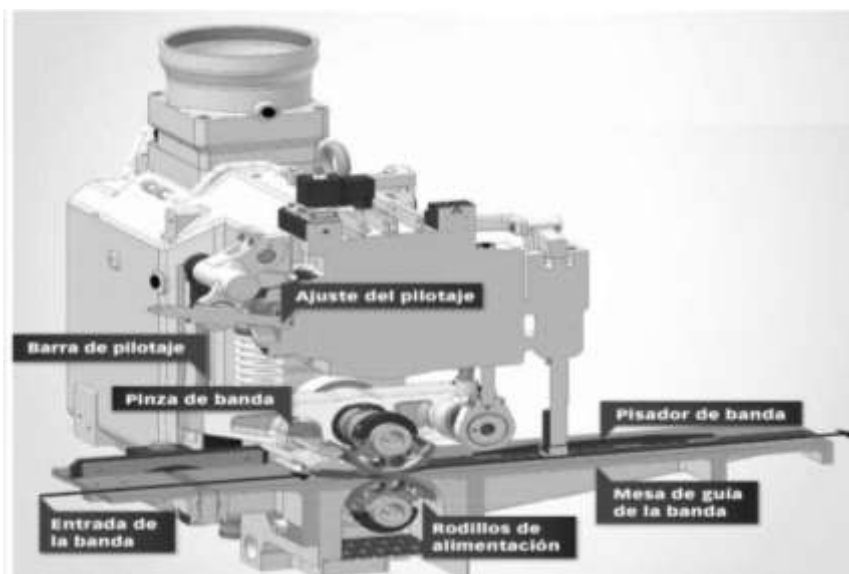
Alimentador mecánico de rodillos BRUDERER. (Bruderer, 2014)
